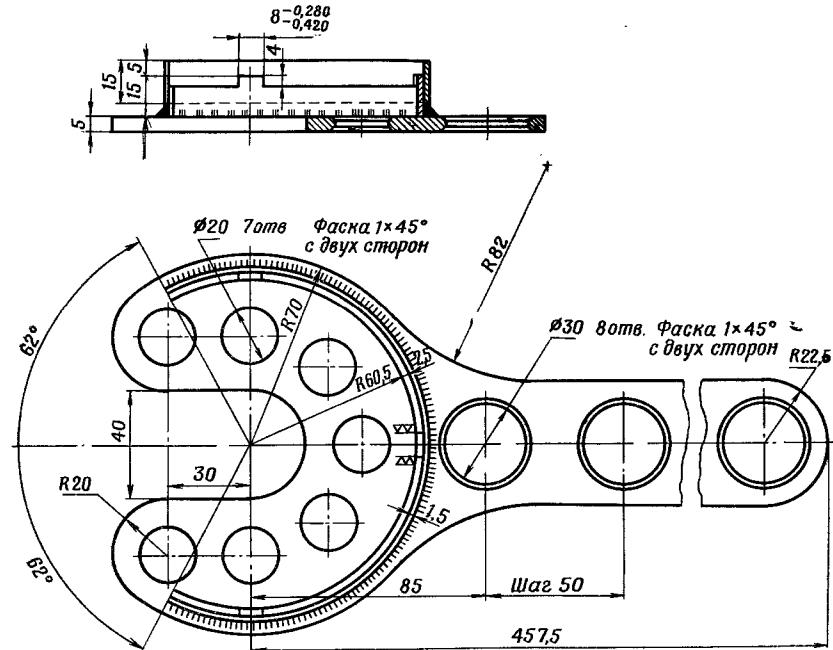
Ключ для уплотнительной гайки поршня цилиндра высокого давления. Материал сталь 10, термически обработать после сварки и цементации головки ключа до $H_{RC} = 40 - 45$, оцинковать
